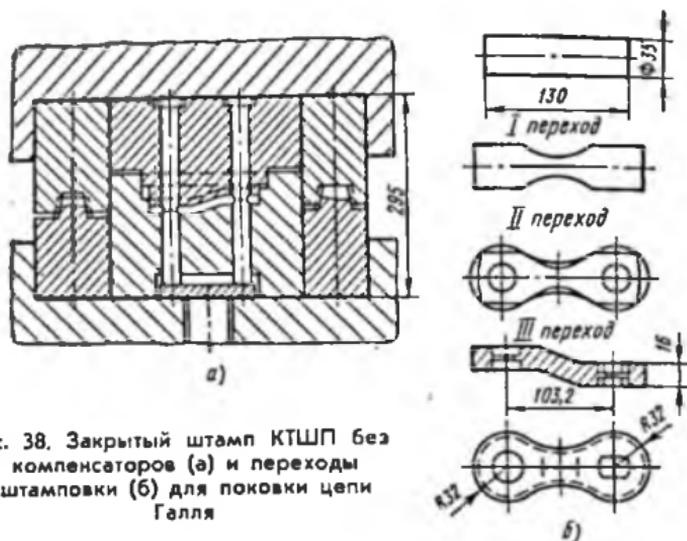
Закрытый штамп КТШП без компенсаторов (а) и переходы штамповки (б) для поковки цепи Галля
